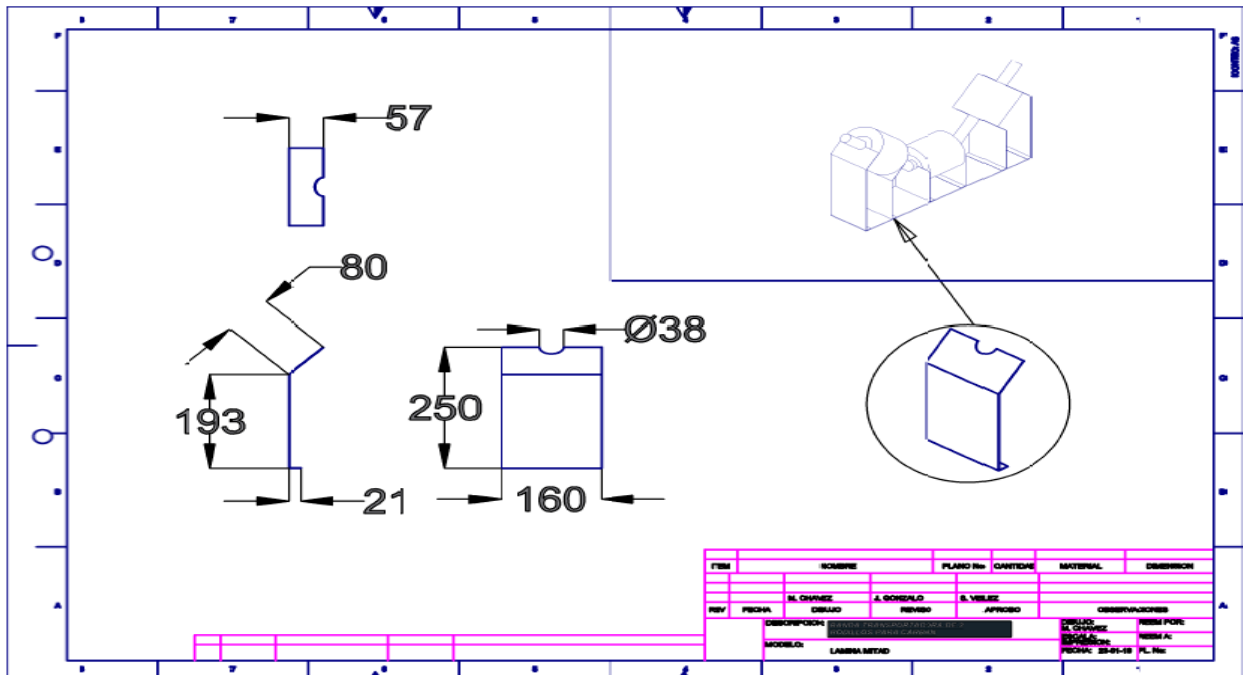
Plano detallado de las láminas verticales internas de soporte de los rodillos.
